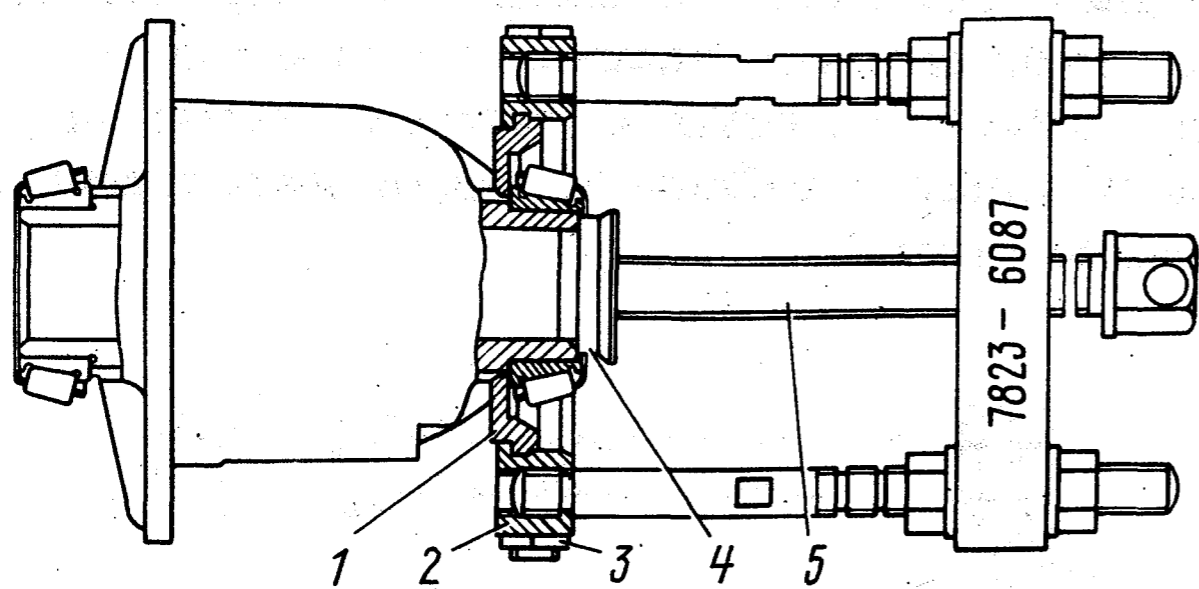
Снятие кольца подшипника с коробки дифференциала: 1 - вкладыш 7823-6101; 2 - опора; 3 - гайка; 4 - подпятник; 5 - винт
